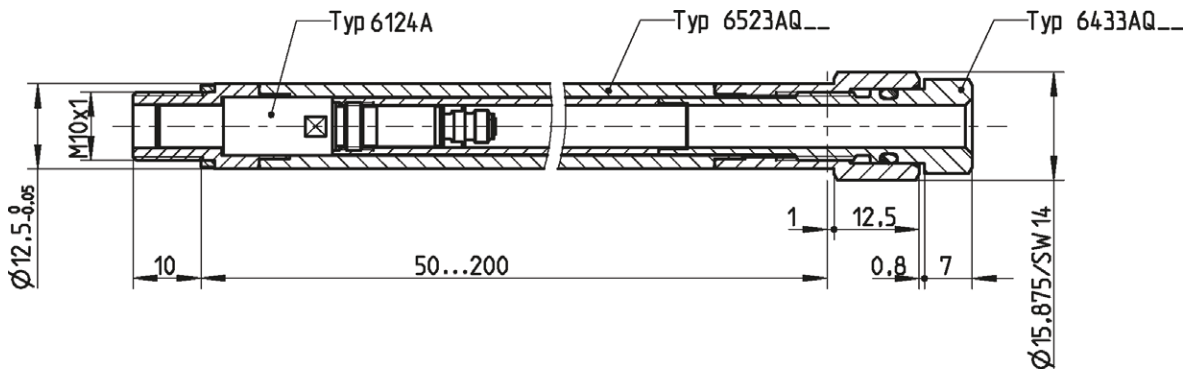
Montagehülse Typ 6523AQ... mit M10x1-Gewinde und Druckstück Typ 6423AQ.
